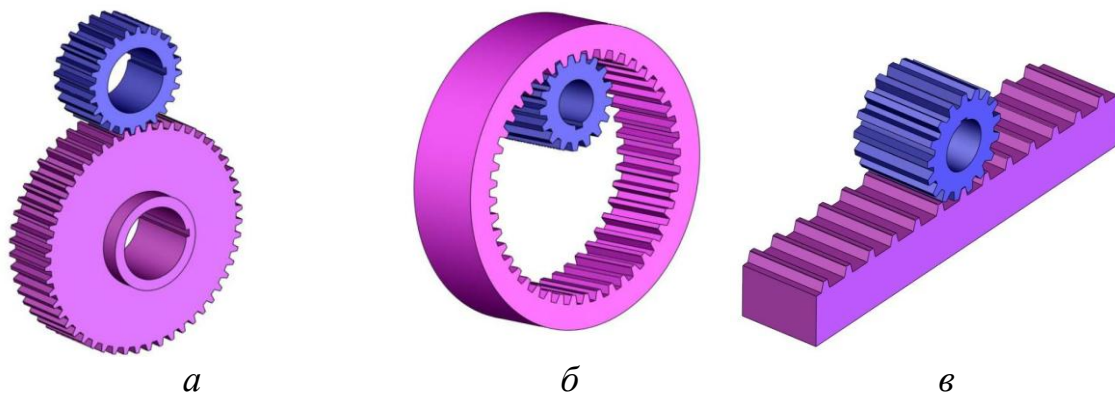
Класифікація зубчастих передач за розташуванням зубців на колесах
